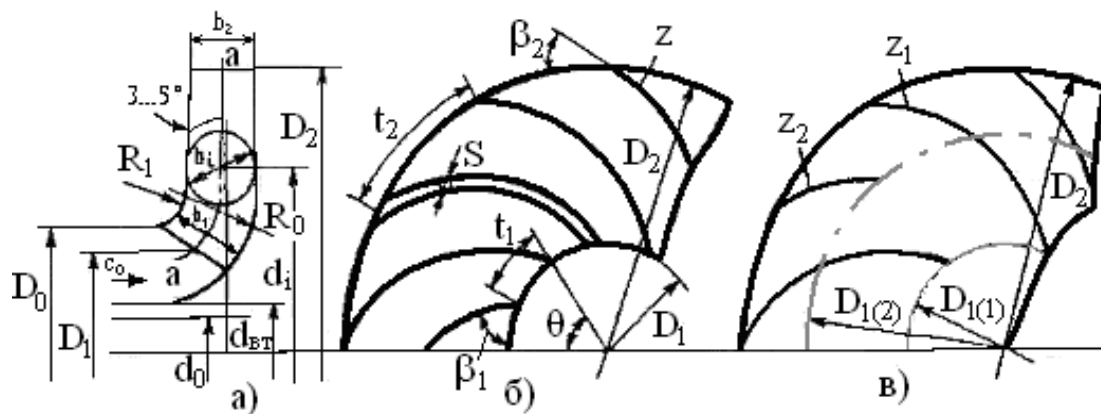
Схема проточной части рабочего колеса центробежного компрессора: а — продольная проекция; б — план лопасти; в — двухъярусная решетка
